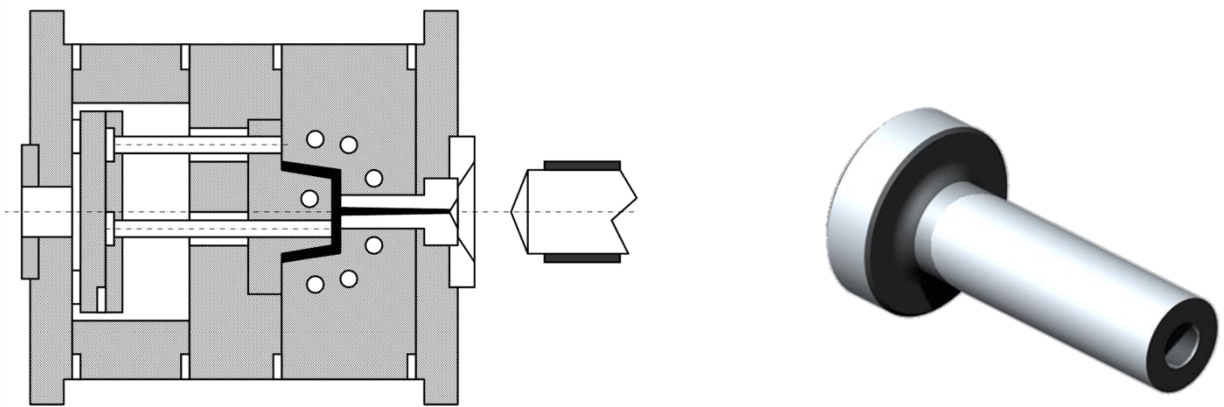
Principe d'alimentation buse machine-buse moule
